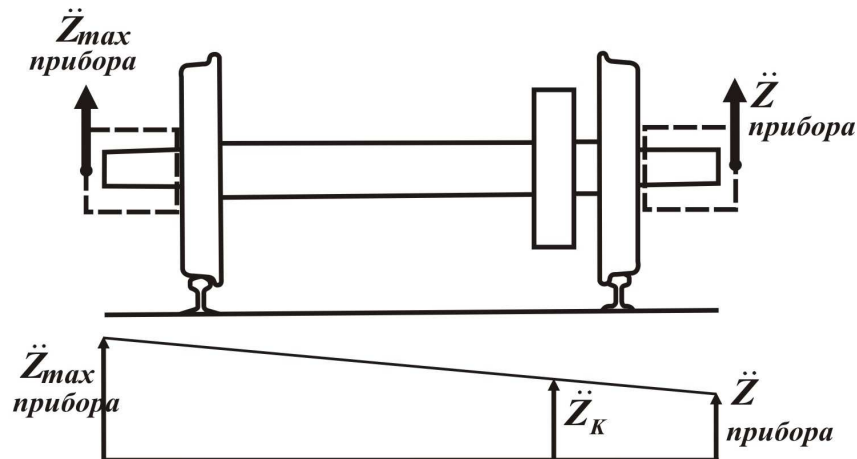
Схема установки датчиков, для измерения ускорений
